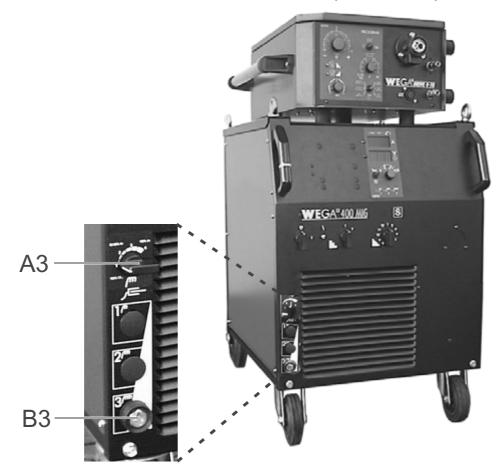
/5; Frontansicht (WEGA 400 MIG E mit elektronischer Drossel)
